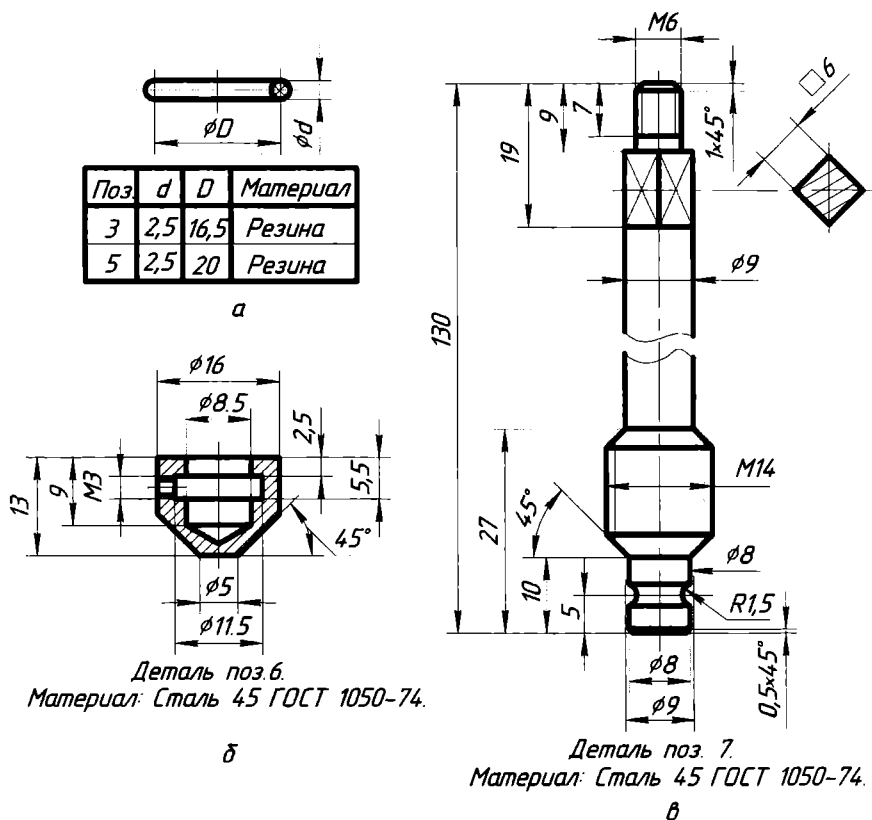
Чертежи: а — кольца; б — клапана; в — шпинделя
